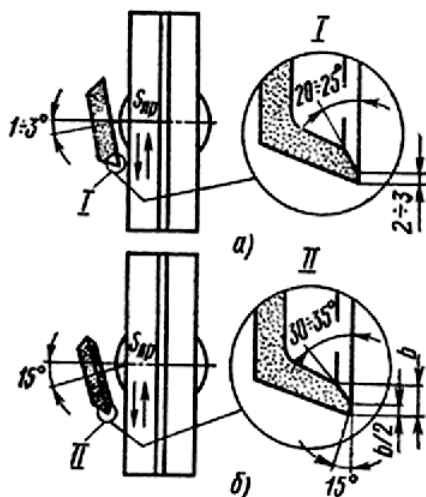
Форма рабочей поверхности шлифовального круга для заточки задних поверхностей зенкеров и разверток:
